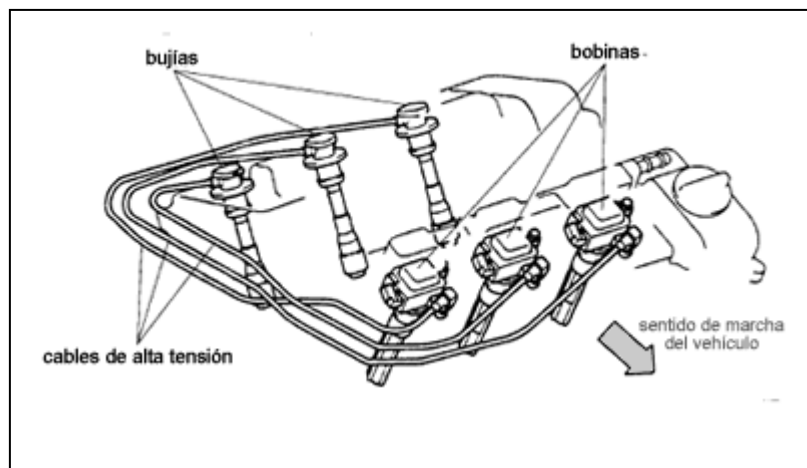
Sistema DIS implantado en un motor en "V" de 6 cilindros.
